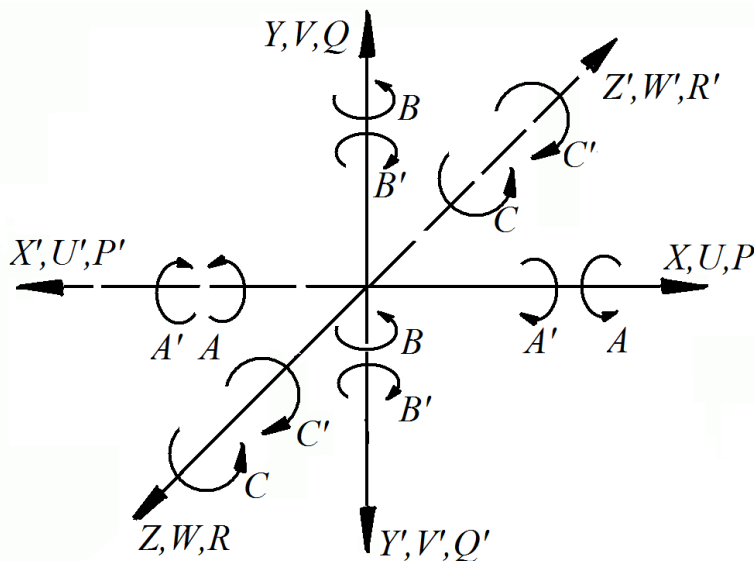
Стандартні системи координат у верстатах з ЧПК
